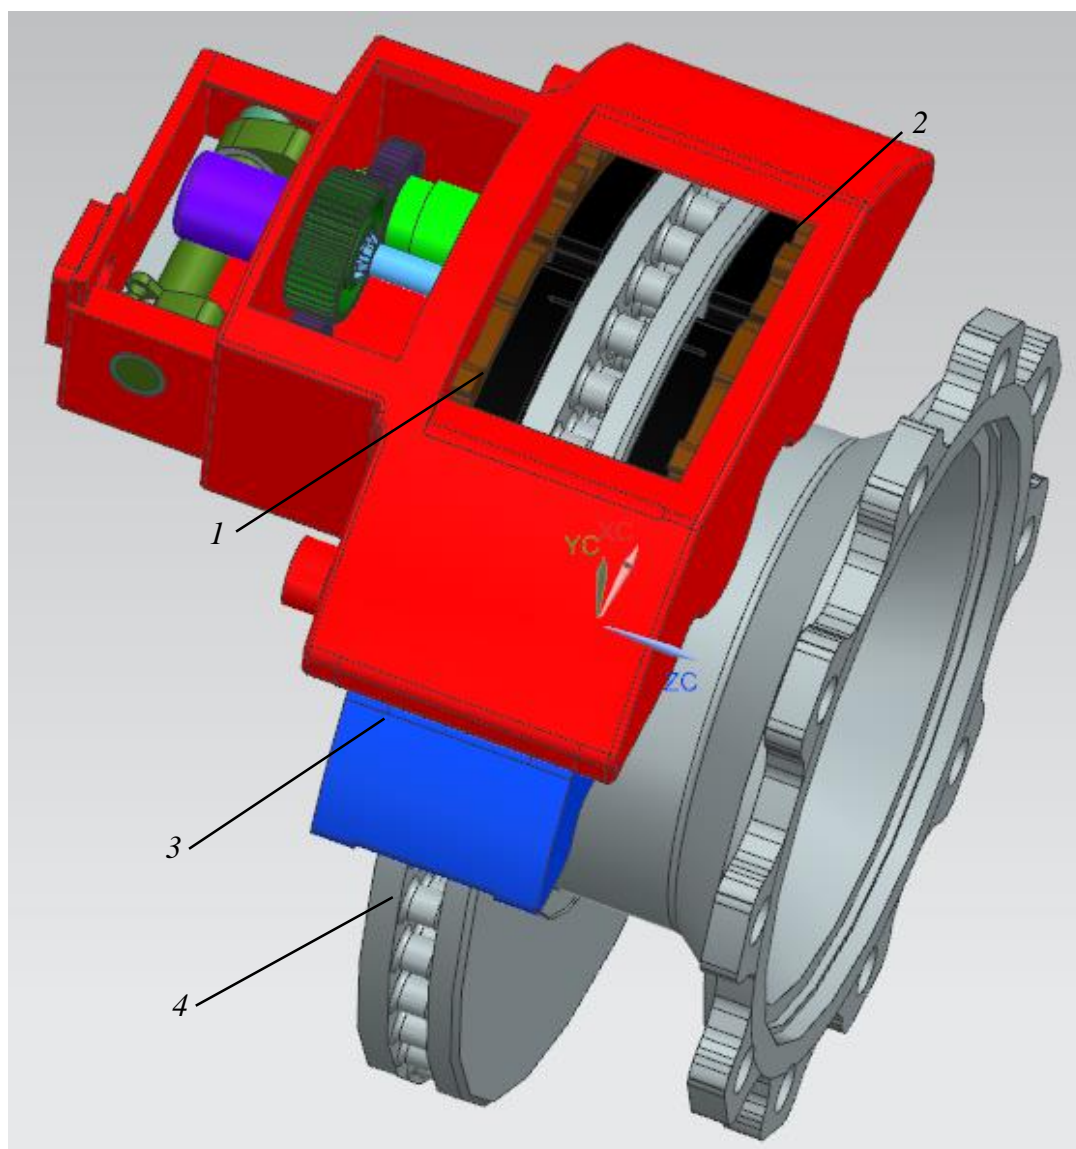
Дисковый тормозной механизм колодочного типа с сегментными колодками:
